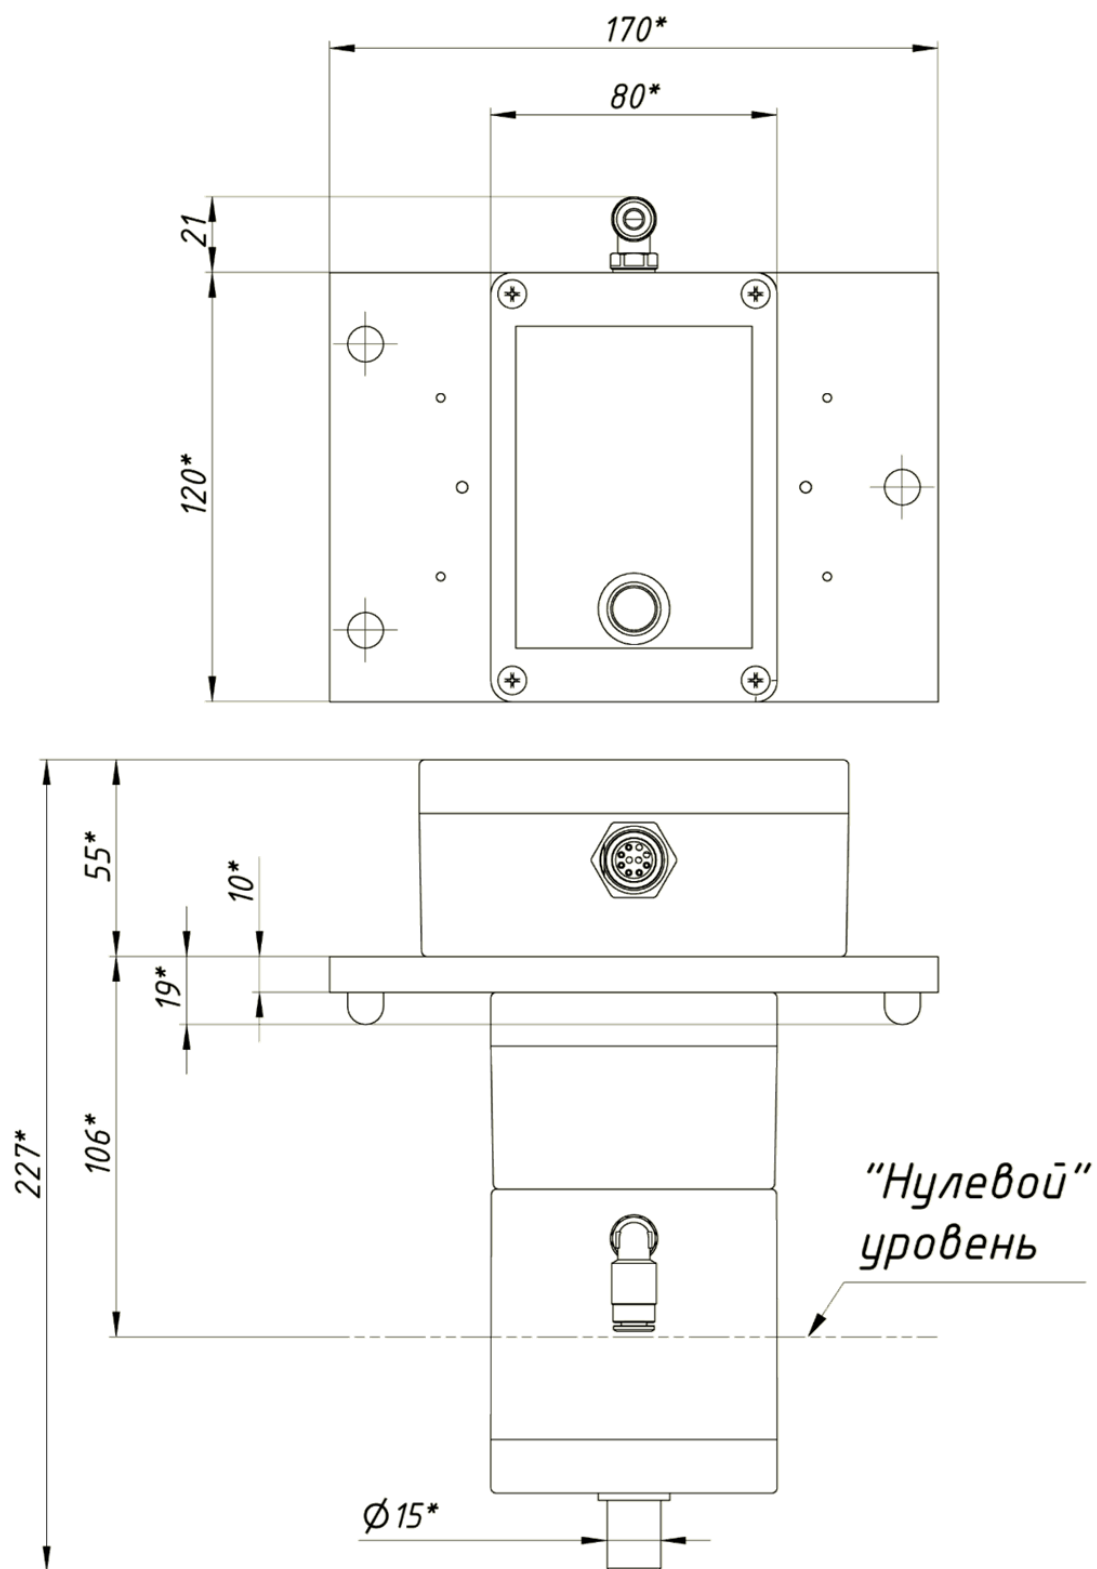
Габаритные и установочные размеры измерителя в исполнении №05.
